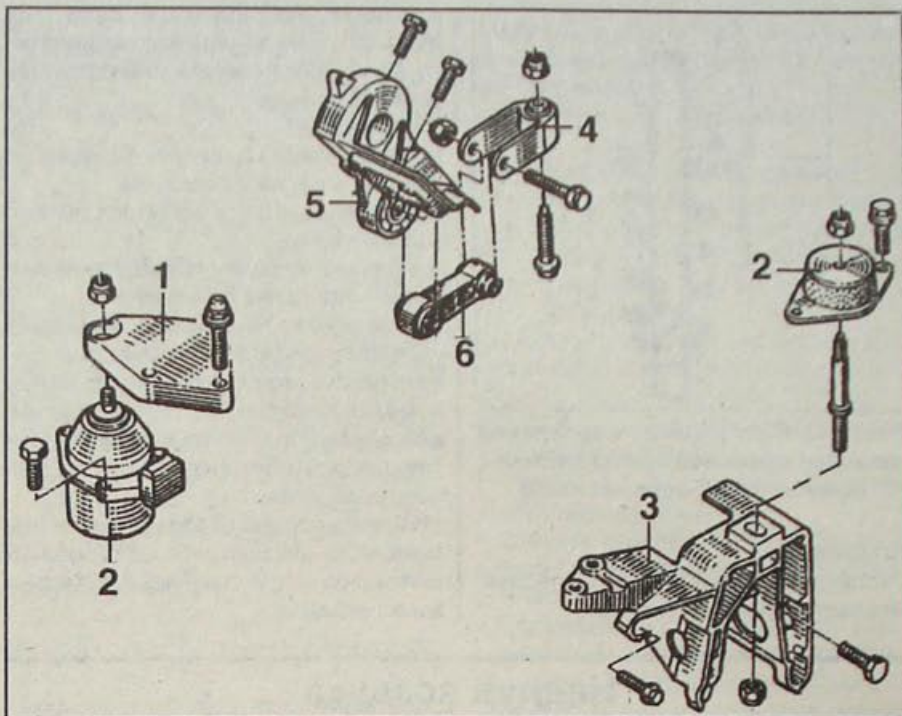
Элементы подвески двигателя/ коробки передач:
